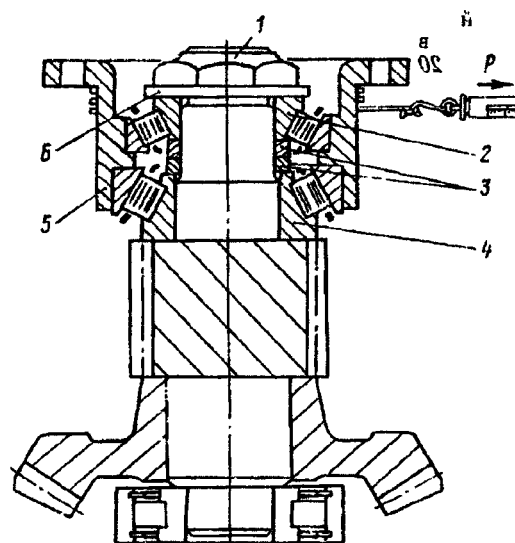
Регулирование подшипника ведущего цилиндрического зубчатого колеса:
